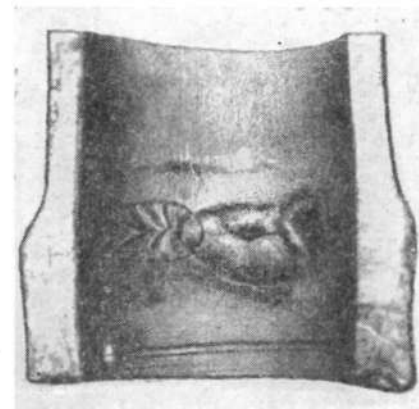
Внешний вид внутреннего валика с кратером, образовавшимся в результате чрезмерного проплавления кромок в начале сварки.
